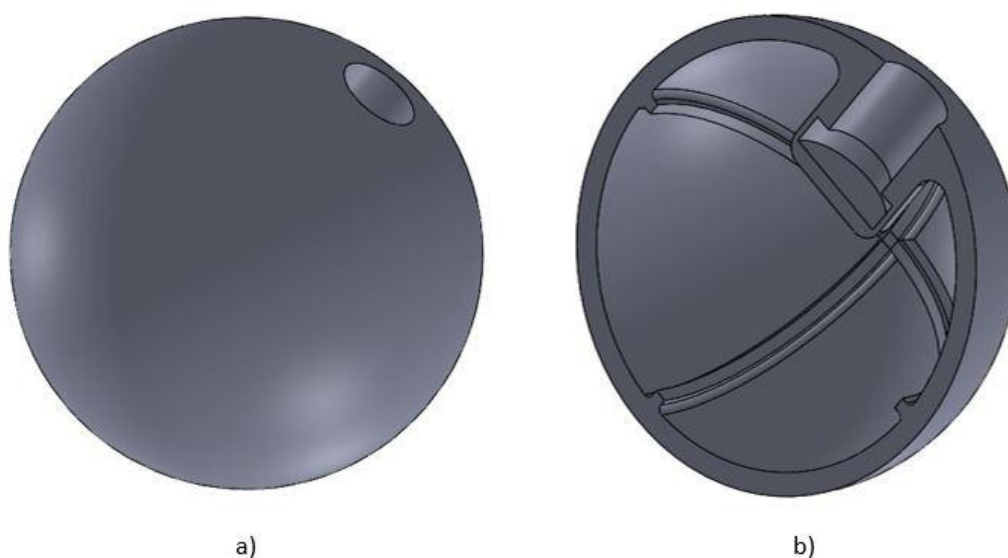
a) Vista Isométrica da Bola; b) Vista em Corte da Bola
